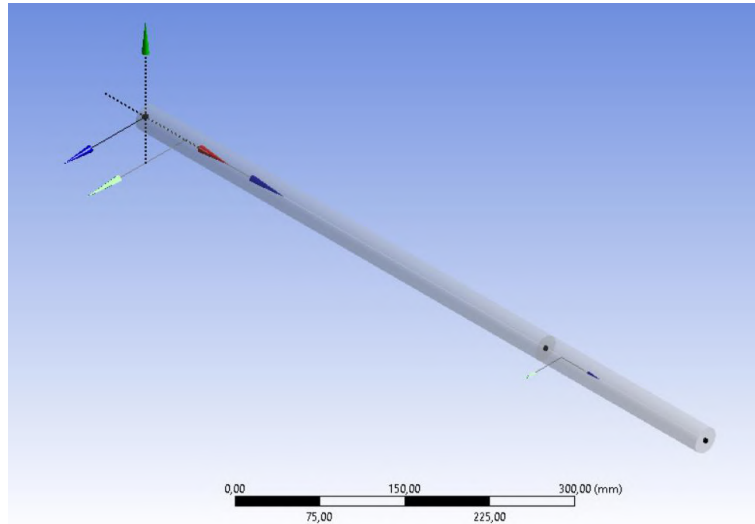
Eje definido como elemento beam en Desing Modeler
